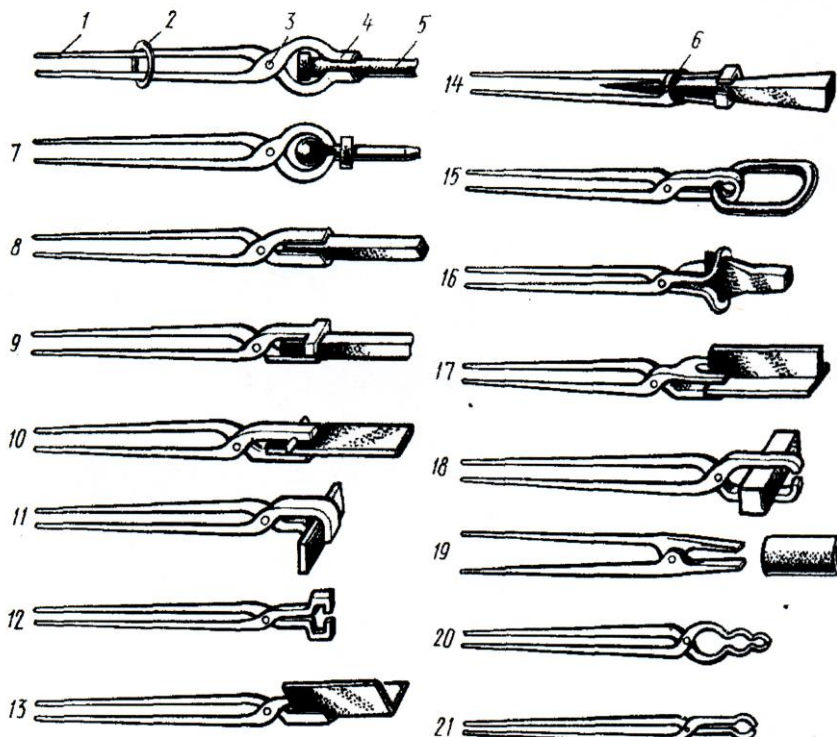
Составные части и виды кузнечных клещей: 1 - рукоятка; 2 - зажимное кольцо; 3 - заклепка; 4 - губки; 5 - заготовка; 6 - петля; 7 - продольно-цилиндрические; 8-10 - продольно-прямоугольные; 11, 12, 18 - поперечно-прямоугольные; 13 - продольно-угловые; 14 - продольно-пирамидальные; 15 - кольцевые; 16 - для топоров; 17 - тавровые; 19 - для захвата цилиндров изнутри; 20, 21 - прутково-поперечные
